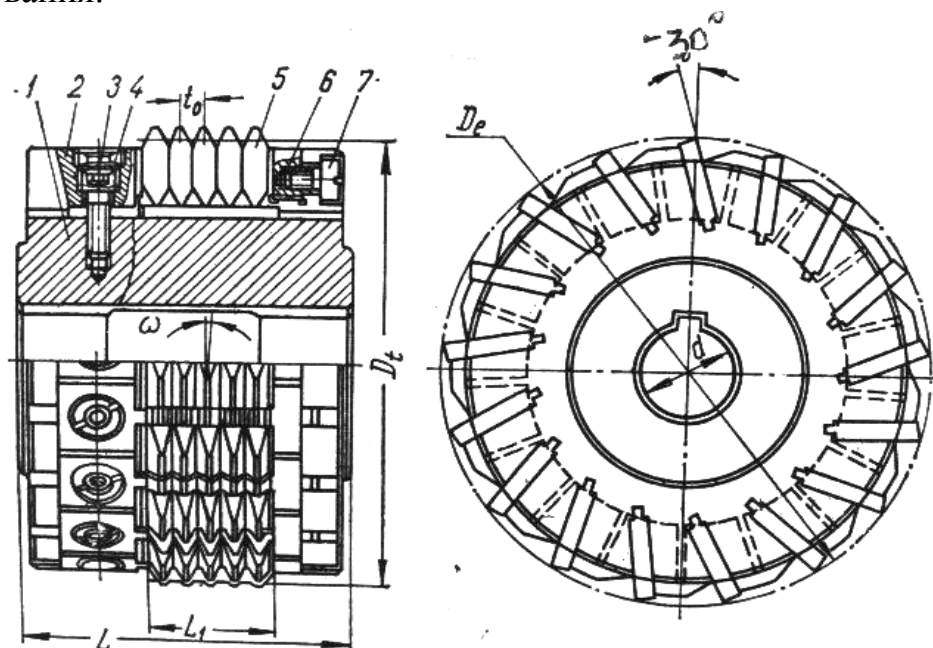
Червячная фреза конструкции КПИ с поворотными пластинками из минералокерамики $m=3,5$ мм.
